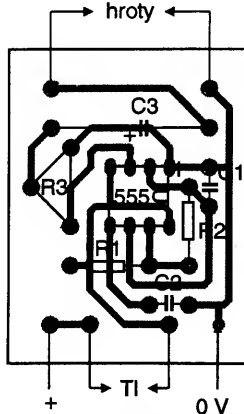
Deska s plošnými spoji C339 pro zapojení z obr. 80 a deska, osazená součástkami ( $C_3 = TE 003$ )
